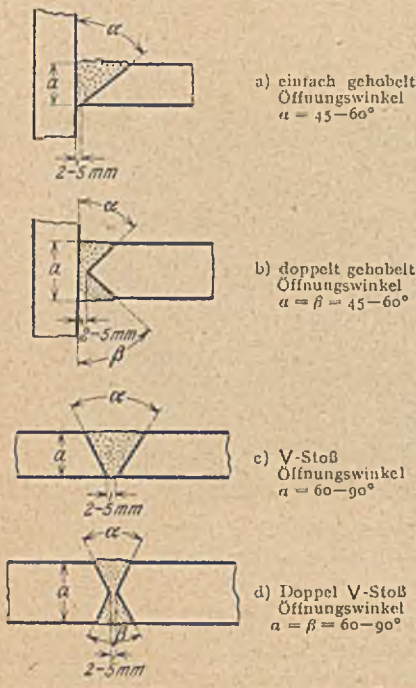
Vier Formen des geschweißten Stumpfstoßes.
